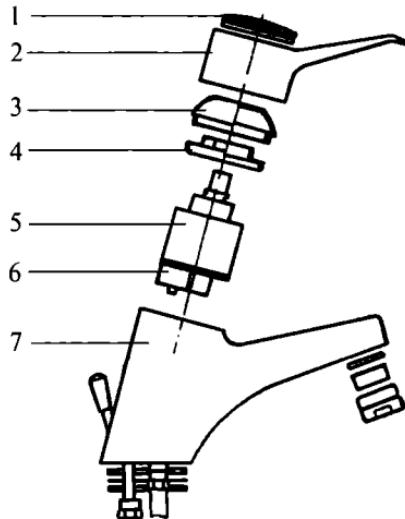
Устройство шарнирного смесителя с аэратором и встроенным фильтром: 1 — фиксирующий элемент; 2 — поворотная рукоятка (джойстик); 3 — крышка корпуса; 4 — круговая гайка; 5 — сменный картридж механической очистки; 6 — прокладка; 7 — корпус
